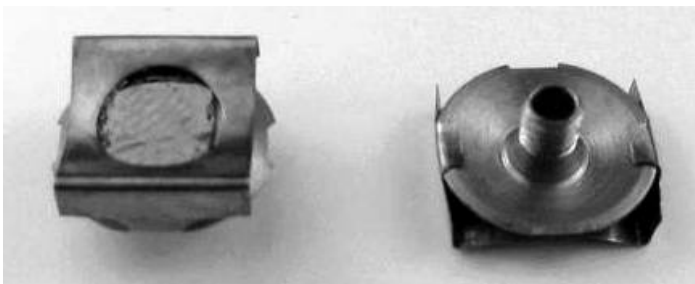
Крепление образца пружинкой, вид сверху и снизу
